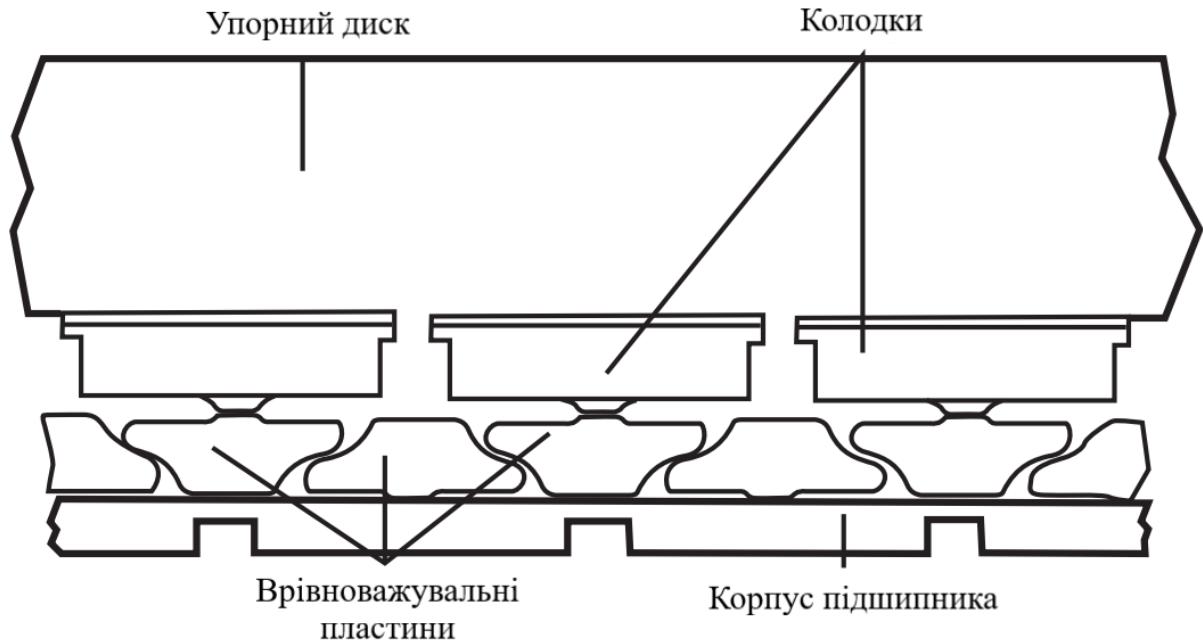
Схема упорного підшипника ковзання[3]
